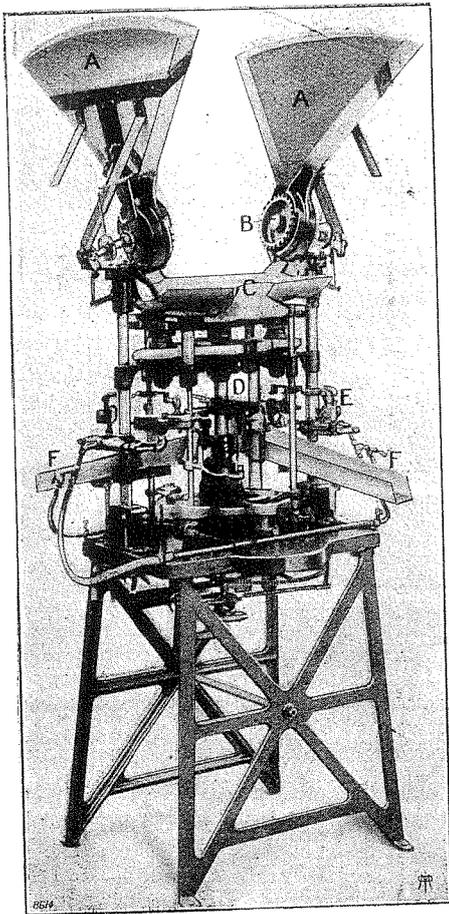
Vue d'une machine à évaser, type double, automatique.
